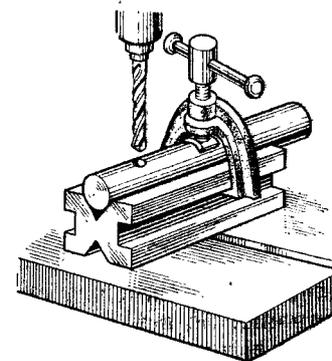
Закрепление цилиндрической детали в призме с зажимным приспособлением
